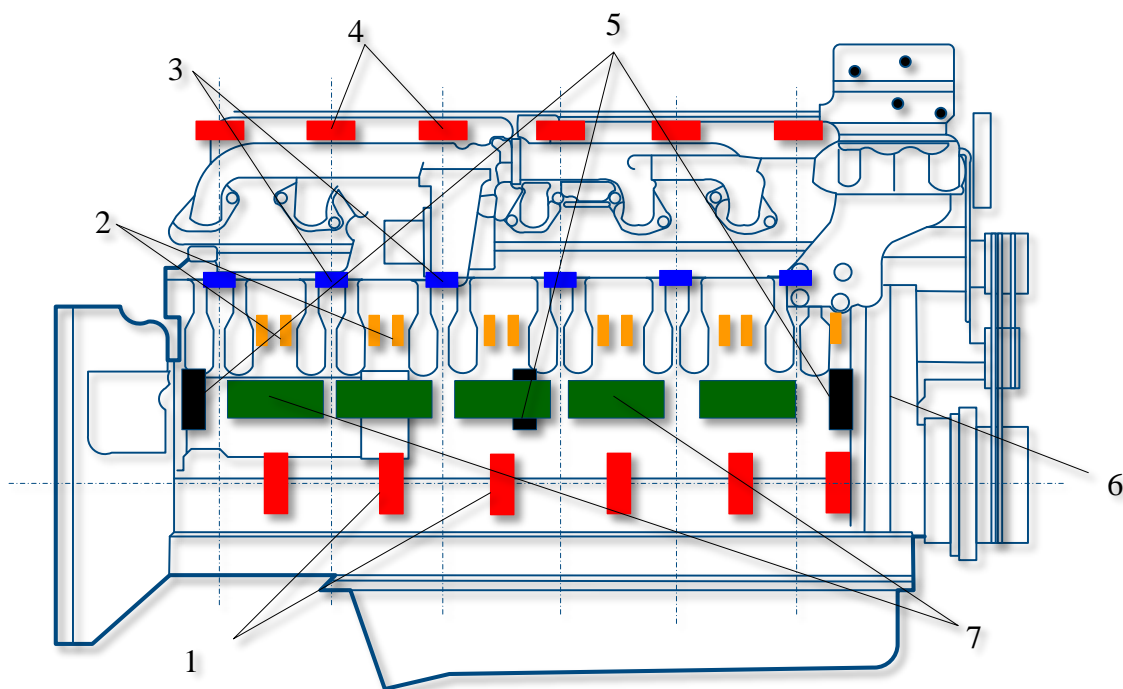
Місця прослуховування сигналів у з'єднаннях двигуна: 1 - колінчастий вал - корінний підшипник; 2 - шатун - втулка; 3 - клапан - днище поршня; 4 - бойок коромисла - стержень клапана; 5 - розподільний вал - підшипник; 6 - розподільні шестерні; 7 - кулачок розподільного валу – штовхач
